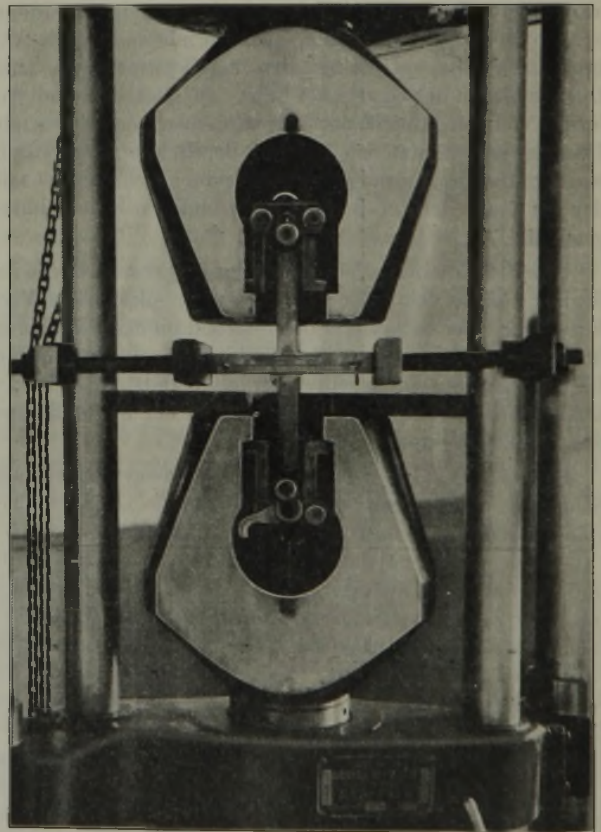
Zweiachsige Beanspruchung einer Aufschweißprobe.
